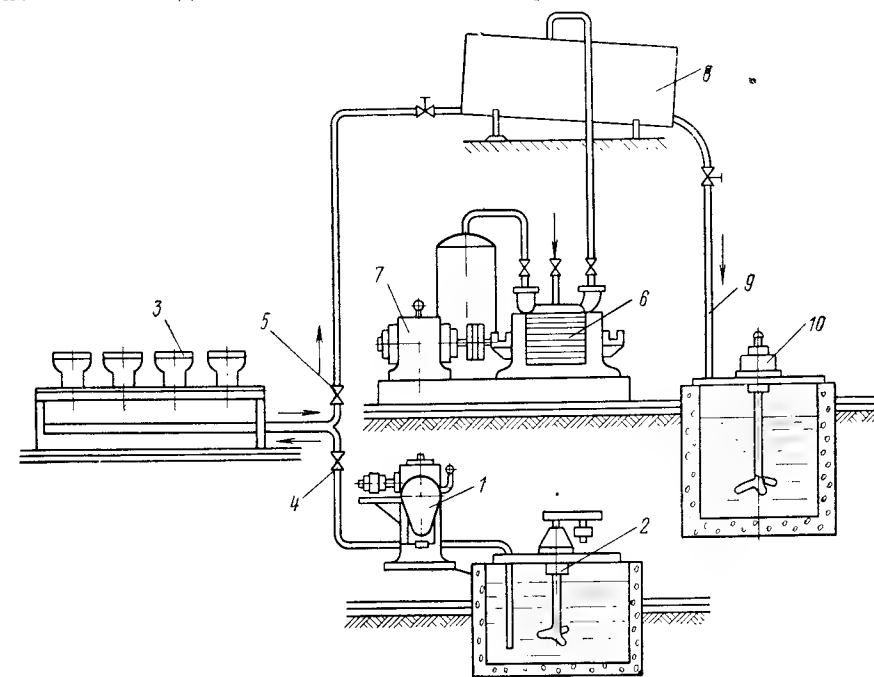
Схема отливки санитарных изделий с вакуумным сливом шликера
